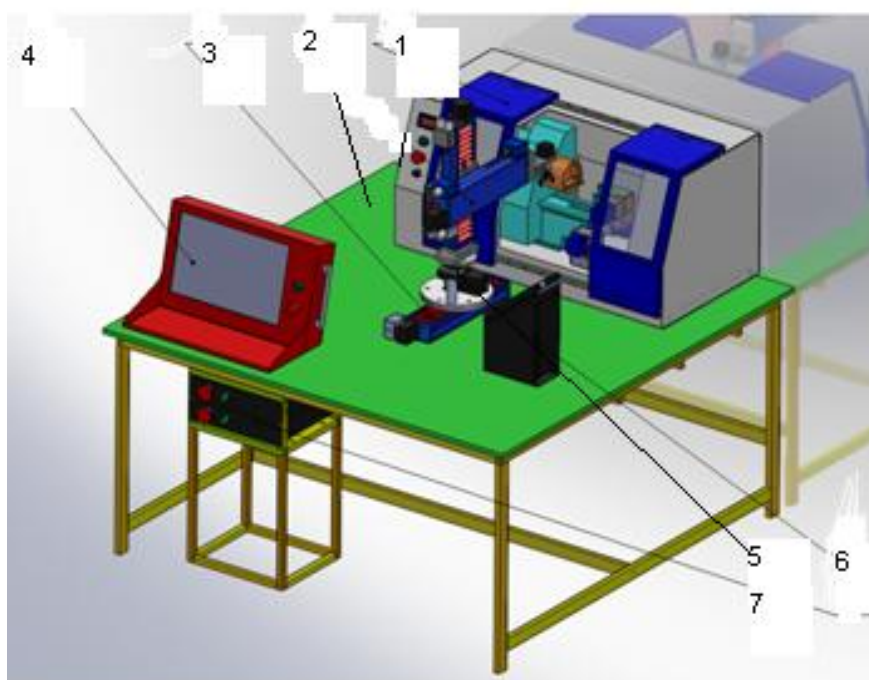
ГПМ на базе токарного станка с компьютерной системой ЧПУ: 1 – станок; 2 – подиум; 3 – стол; 4 – ноутбук; 5 – робот; 6 – накопитель; 7 – блок управления
